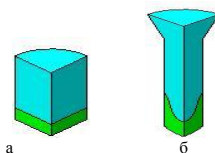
Заготовка із поперечною шаруватістю, отримана видавлюванням: а – вихідна заготовка; б - деталь
